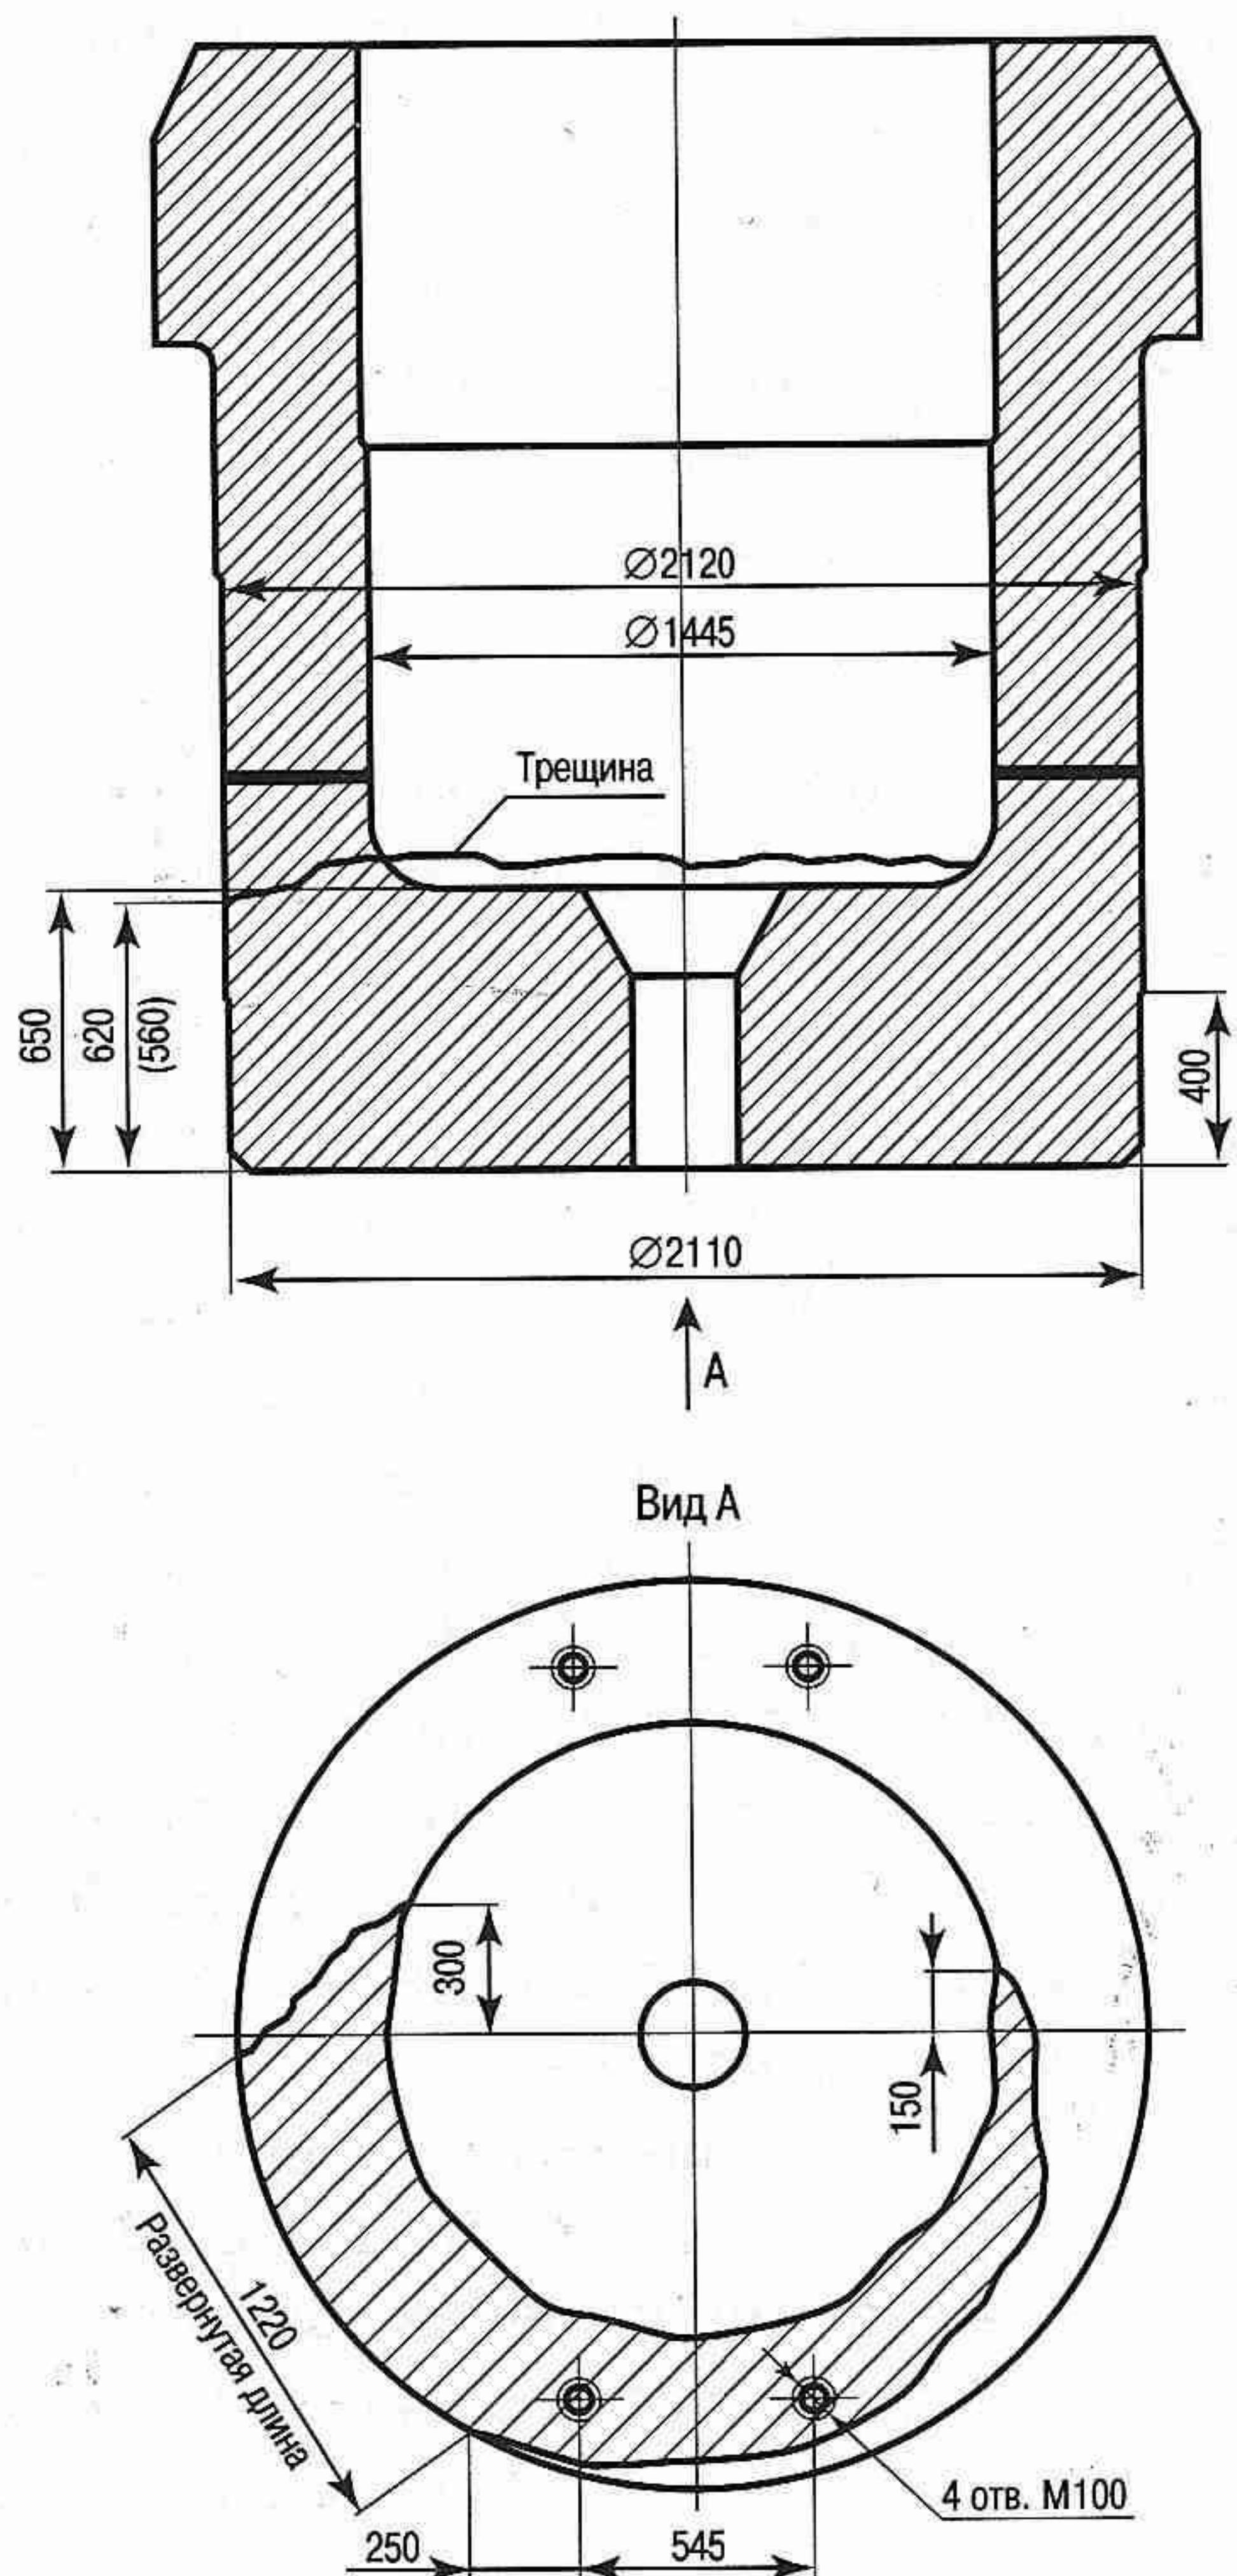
Трещина в днище сварнокованного цилиндра пресса усилием 50 МН
